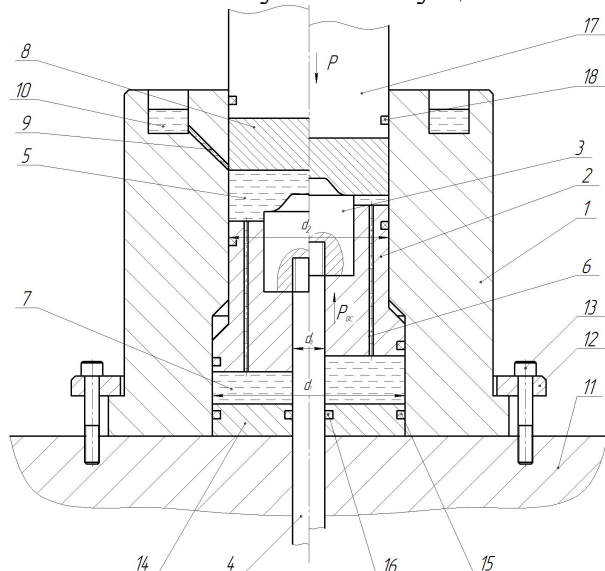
Штамп для виготовлення порожнин в заготовках з важкодеформівних матеріалів.
